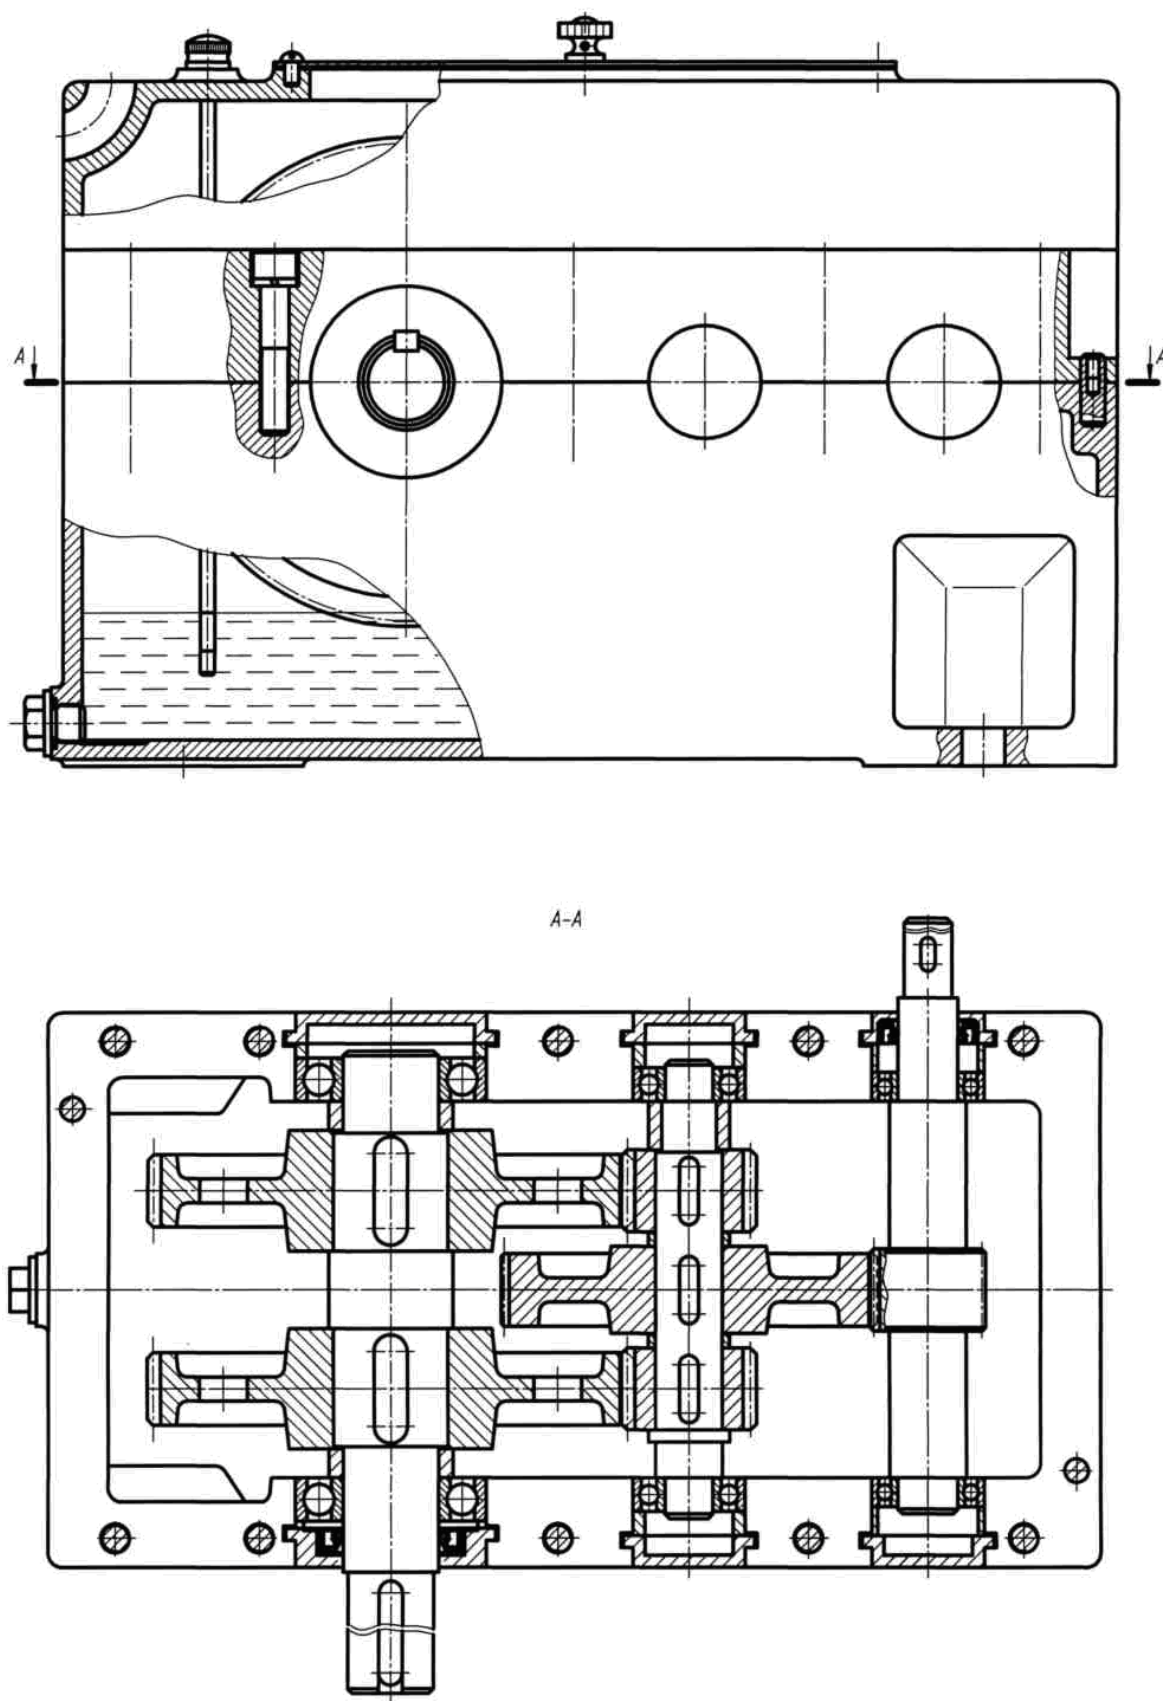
Редуктор двухступенчатый цилиндрический с раздвоенной
